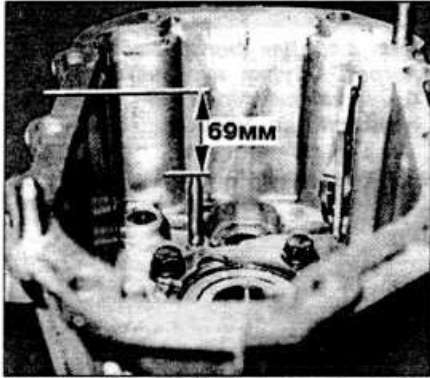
При замене задней крышки коробки передач установить новый стопорный палец штока выбора и переключения передач, выдержав размер, равный 69 мм, между торцом пальца и сопрягающейся поверхностью крышки
